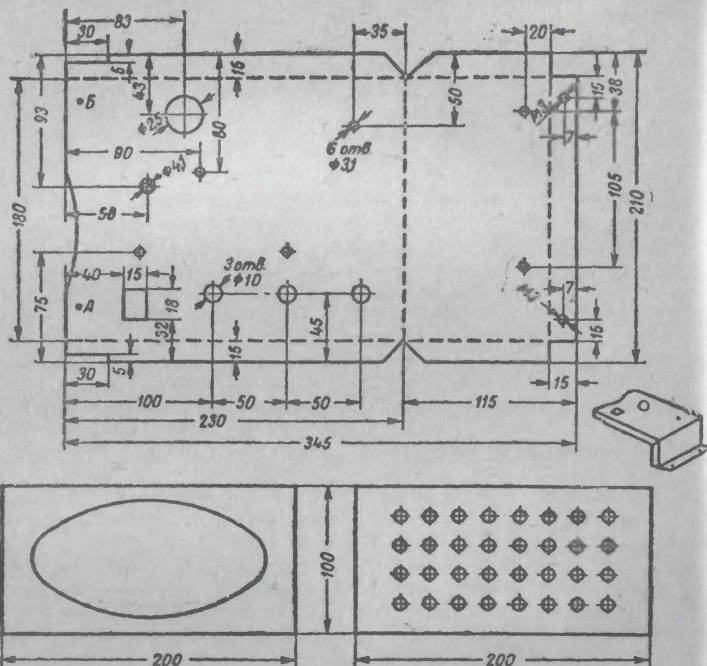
Конструкция корпуса панели магнитофонной приставки.
